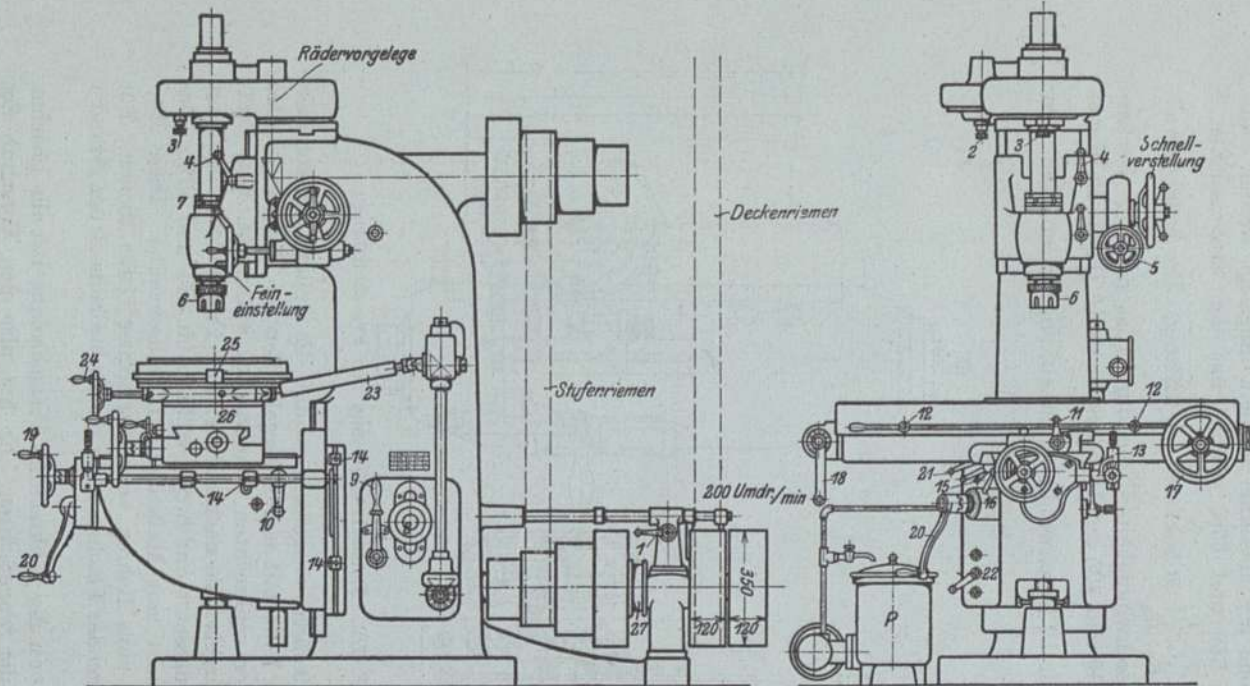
und 578. Senkrechte Fräsmaschine. Gildemeister &amp; Co., A.-G. Bielefeld.
